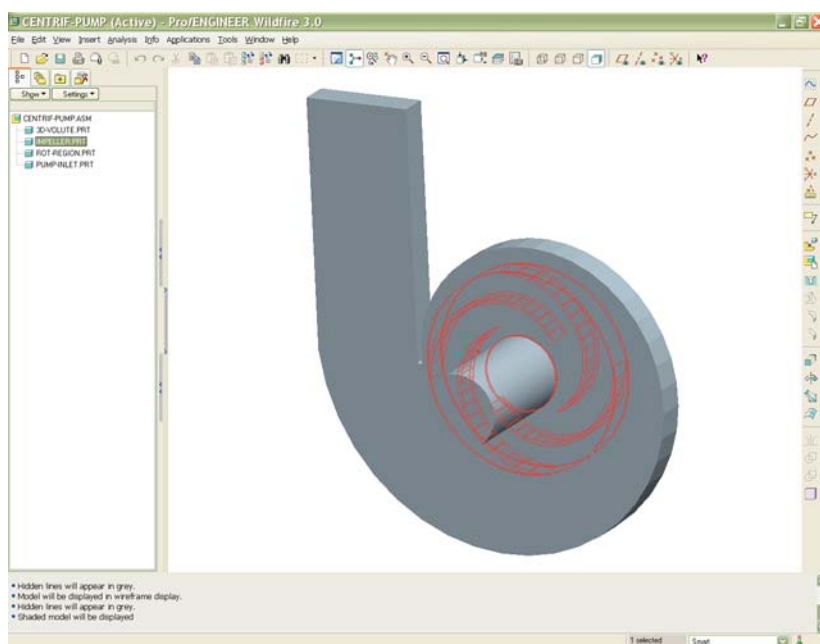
3D модель центробежного насоса в Pro/ENGINEER
